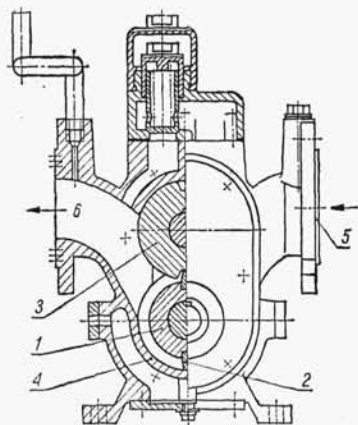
Pompa krzywkowa firmy Stothert i Pitt do olejów i innych cieczy gęstych (melasa, mydło, glukoza itp.); 1 — wirnik zewnętrzny, 2 — wirnik wewnętrzny, 3 — kadłub, 4 — zawór bezpieczeństwa
